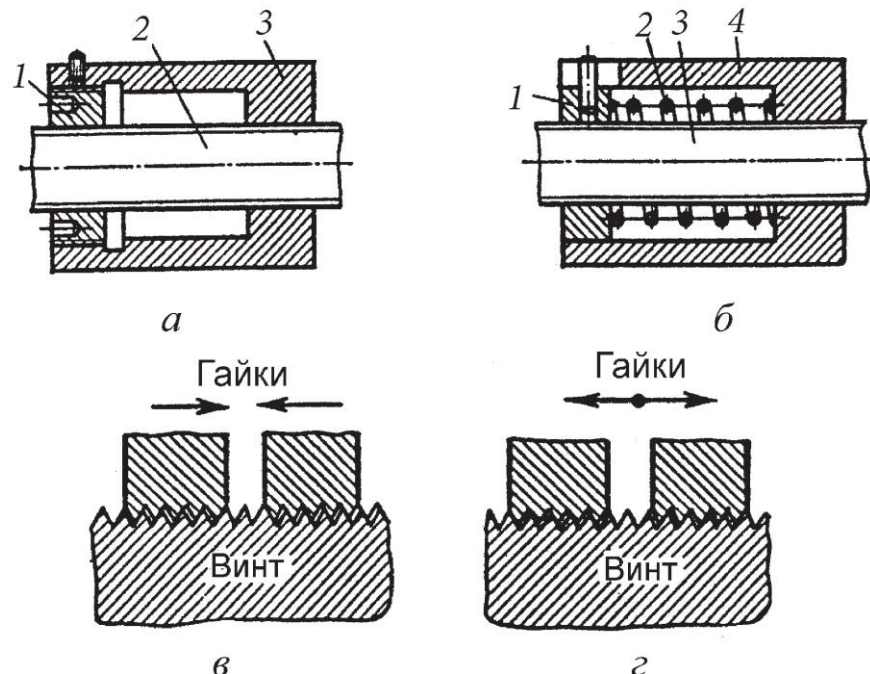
Механизмы для выборки осевой составляющей бокового зазора
